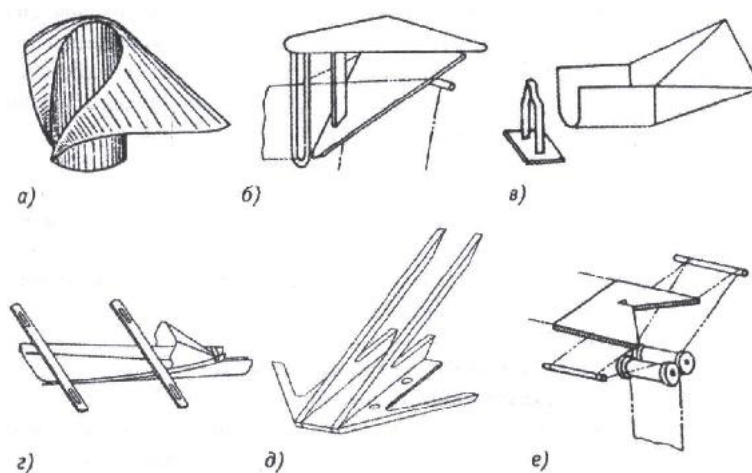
Схеми типових конструктивних елементів пристроїв для формування упаковки із термозварних рулонних пакувальних матеріалів:
